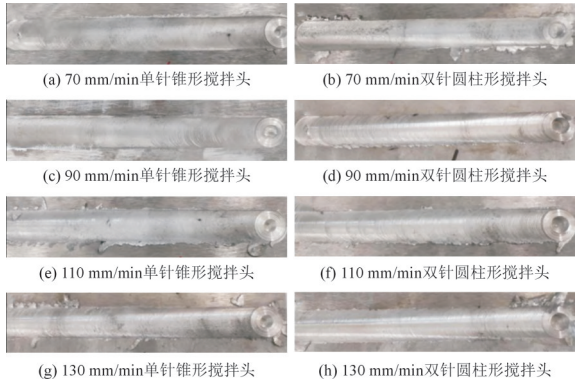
不同焊接速度下 FSW 接头的表面形貌^[34]
